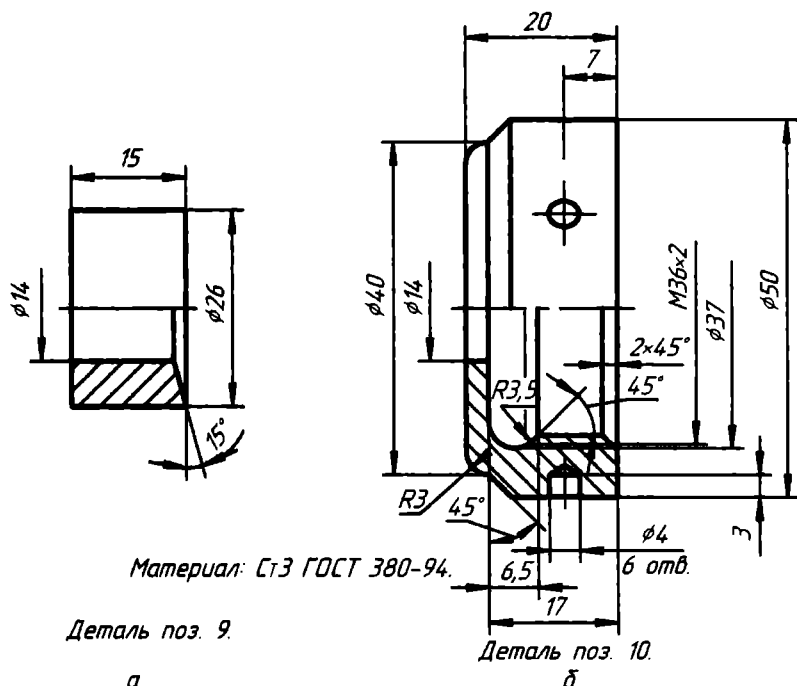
Чертежи: а — нажимной втулки; б — гайки
